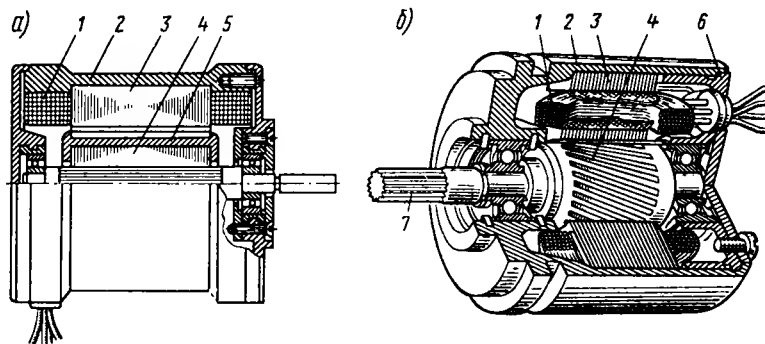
Устройство исполнительного двигателя с беличьей клеткой на роторе:
